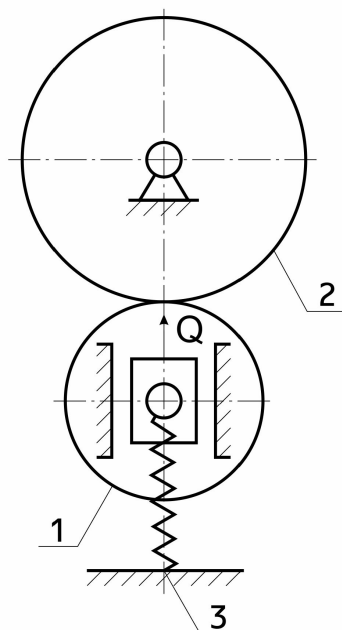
Фрикционный механизм с цилиндрическими катками
